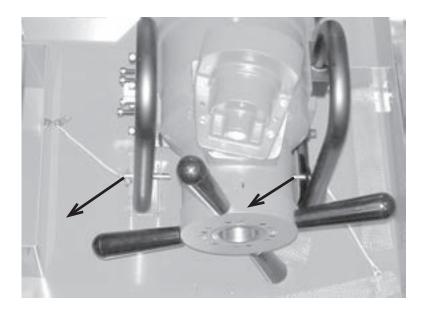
Deux goupilles de fixation sont fournies pour fixer la machine dans sa caisse de rangement. Introduisez les goupilles dans les supports de la caisse et la poignée de la machine EP 424 lorsque vous rangez la machine.
